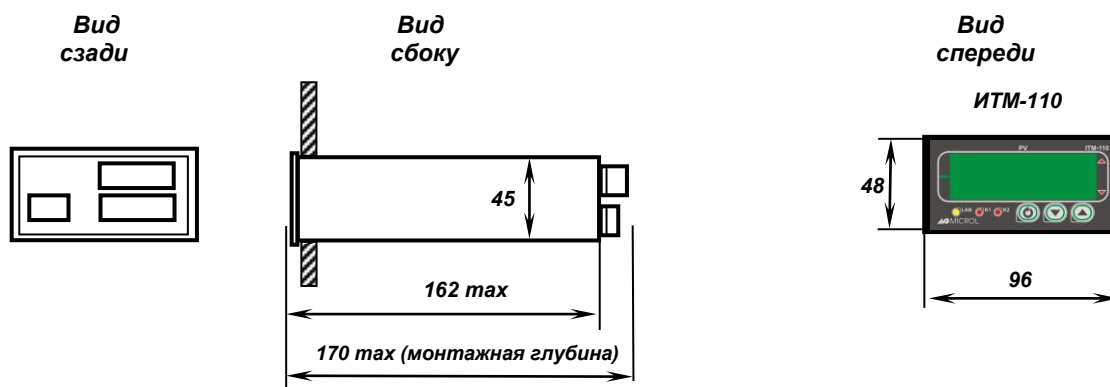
Внешний вид индикатора ИТМ-110
